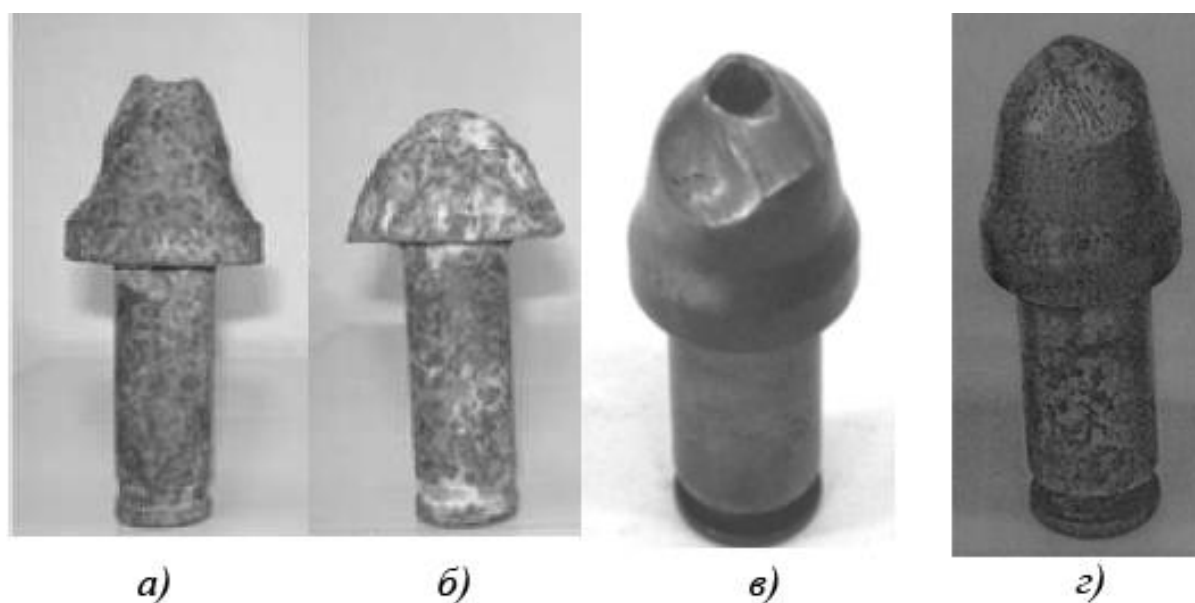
Вид поворотных резцов после отрыва твердосплавной вставки: а, б) зарубежный производитель (*Alpine*); в, г) отечественный производитель (ОАО «Горный инструмент» резец РШ 32-70/16SK).
